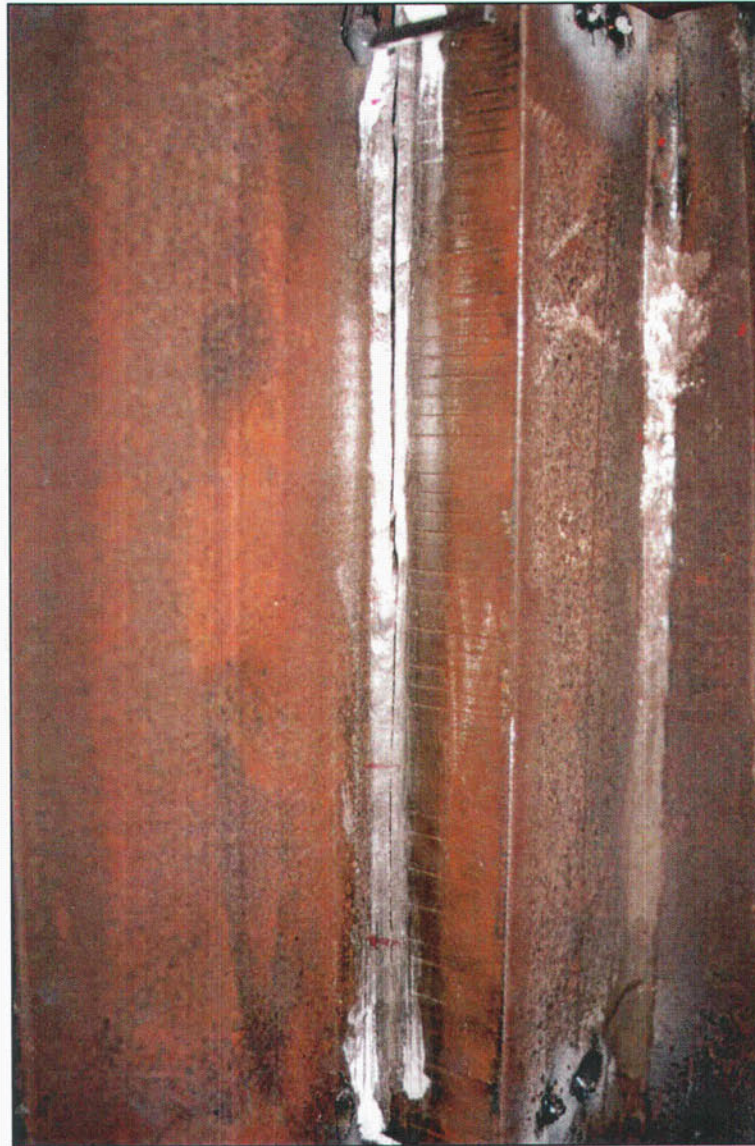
Detalle de la probeta 5S ya rota, con las soldaduras limpias de cal. Se observa claramente el plano de garganta roto en la soldadura 2-4.
